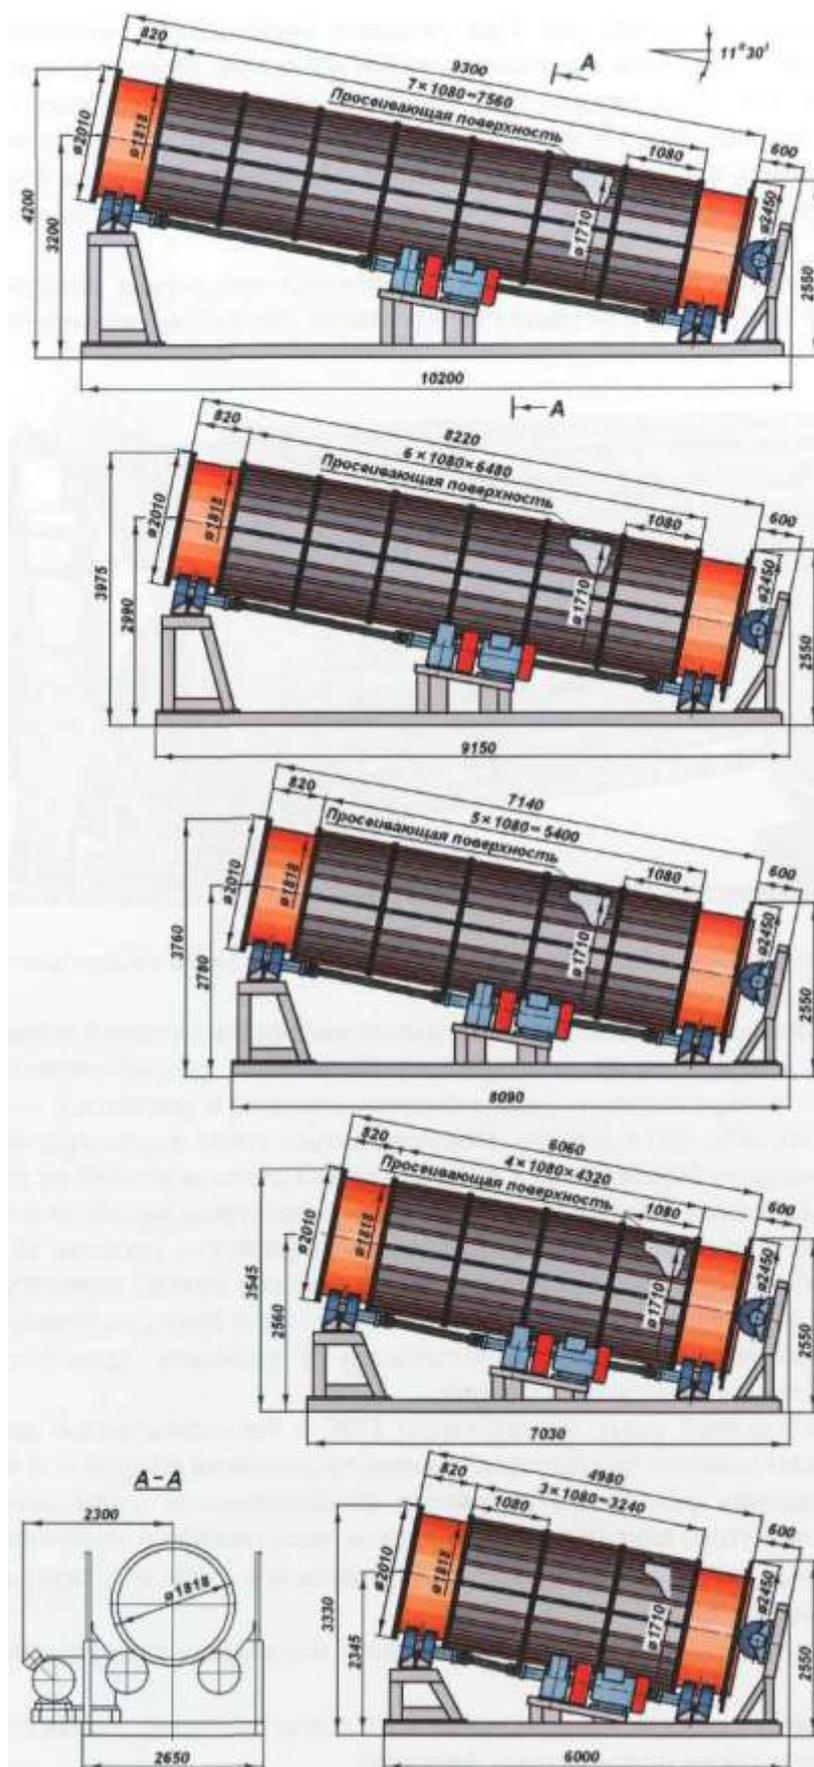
Типоразмерный ряд барабанных грохотов с «двухплечевым» приводом от одного электродвигателя и рабочими поверхностями СДАЛ.
